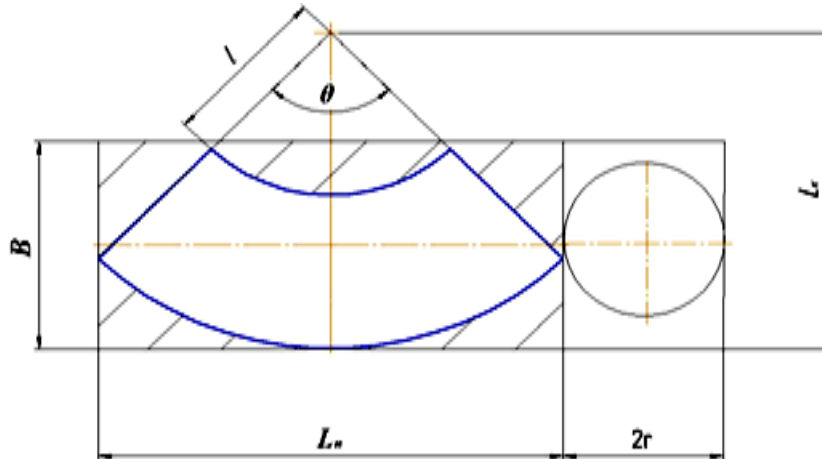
Форма заготовки для виготовлення конічного напівфабрикату
